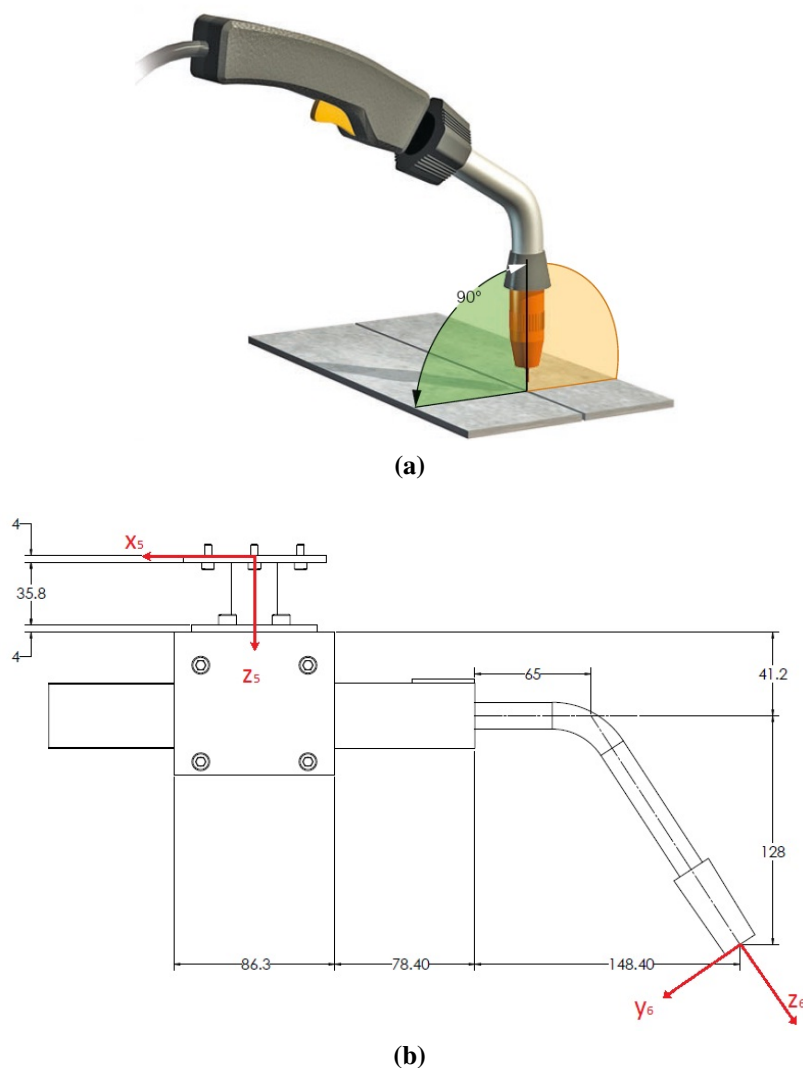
Esquemas del efector final una vez ubicado en el robot. a) Posición deseada del efector final para realizar la soldadura. Fuente [15]. b) Medidas y ejes cartesianos del efector final para el modelamiento.
